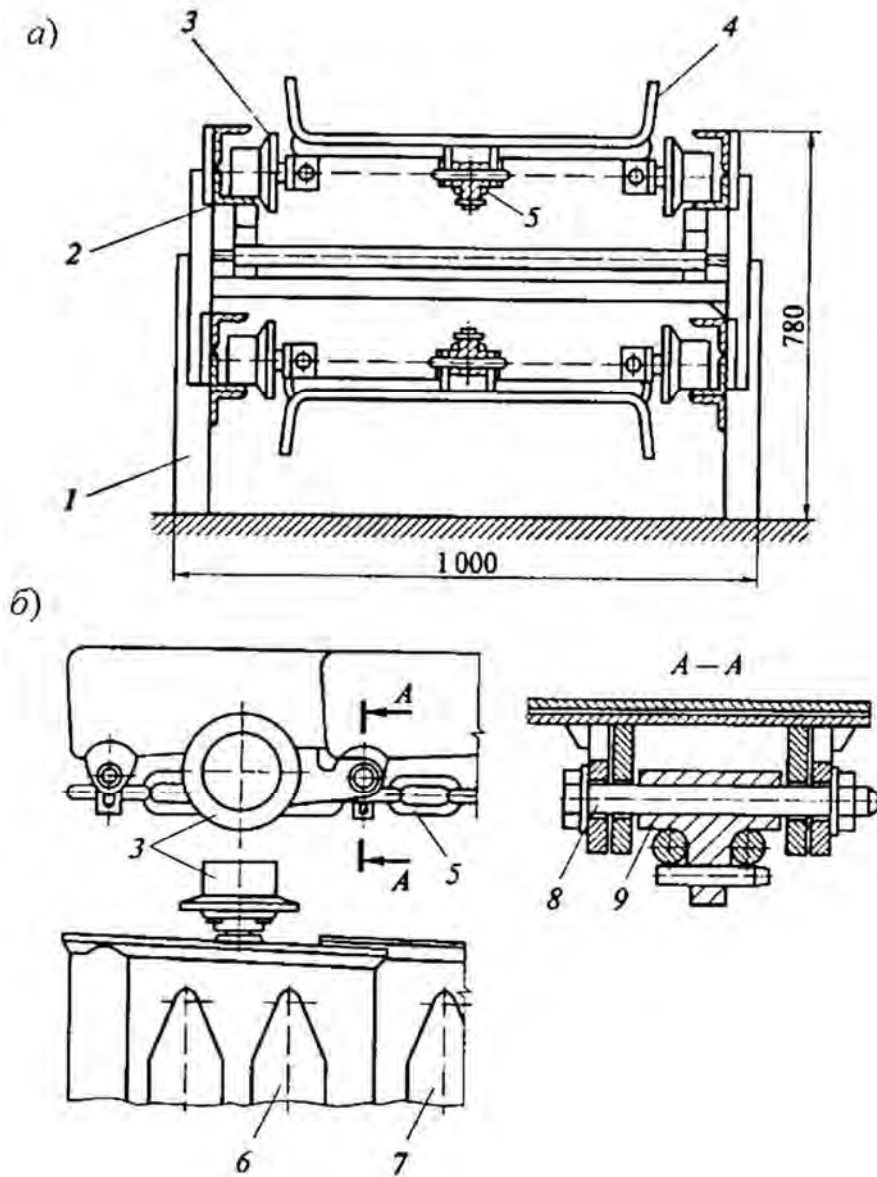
Изгибающийся пластинчатый конвейер: *a* – поперечное сечение; *б* – ходовая часть; 1 – опорная рама; 2 – направляющий путь; 3 – каток; 4 – пластинчатое полотно; 5 – тяговая цепь; 6 – катковая пластина; 7 – бескатковая пластина; 8 – ось; 9 – поводок
